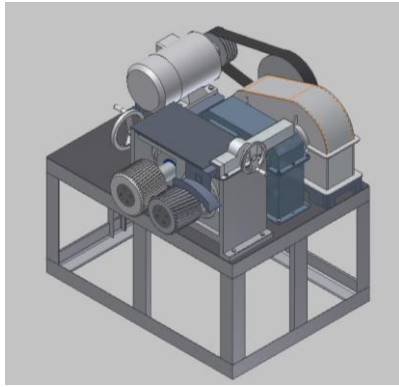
Vista frontal en 3D de la Maquina Destalonadora
